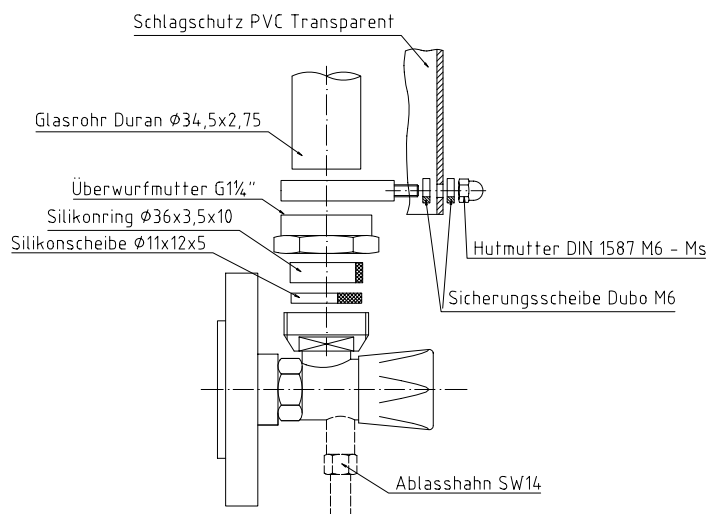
Zusammenbau GNR5 mit Flanschanschluss
